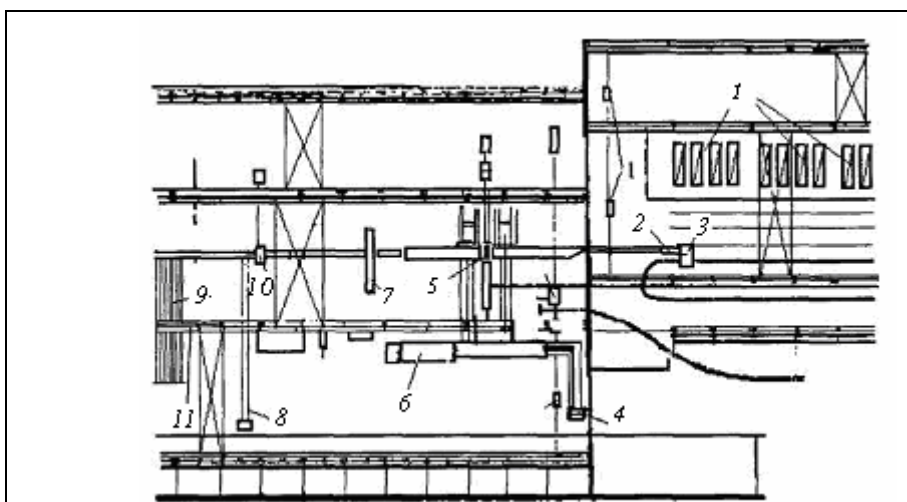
Схема расположения оборудования блюминга 1300 ОАО «Северсталь»:
